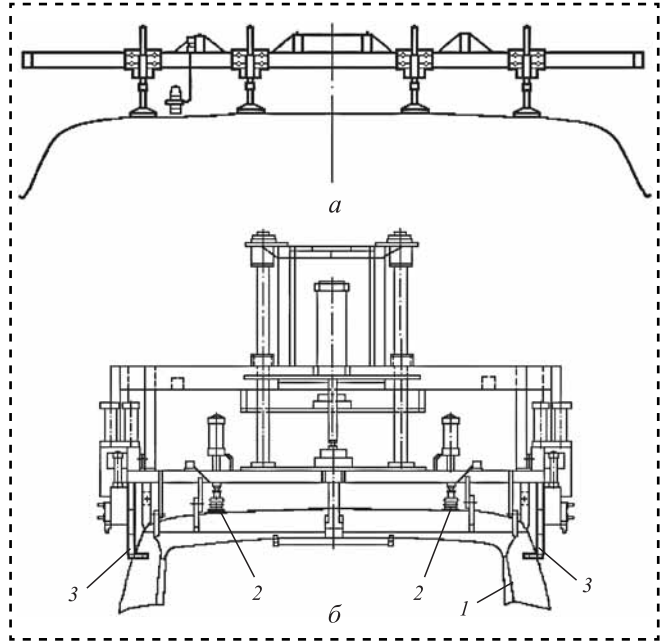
Схема размещения присосок вакуумного захвата по ширине крыши кабины автомобиля "ГАЗель" (а) и конструкция поддерживающего вакуумного захвата загрузочного робота для крыши кабины автомобиля "ГАЗель" (б): 1 — крыша; 2 — присоска; 3 — поддерживающий уголок
